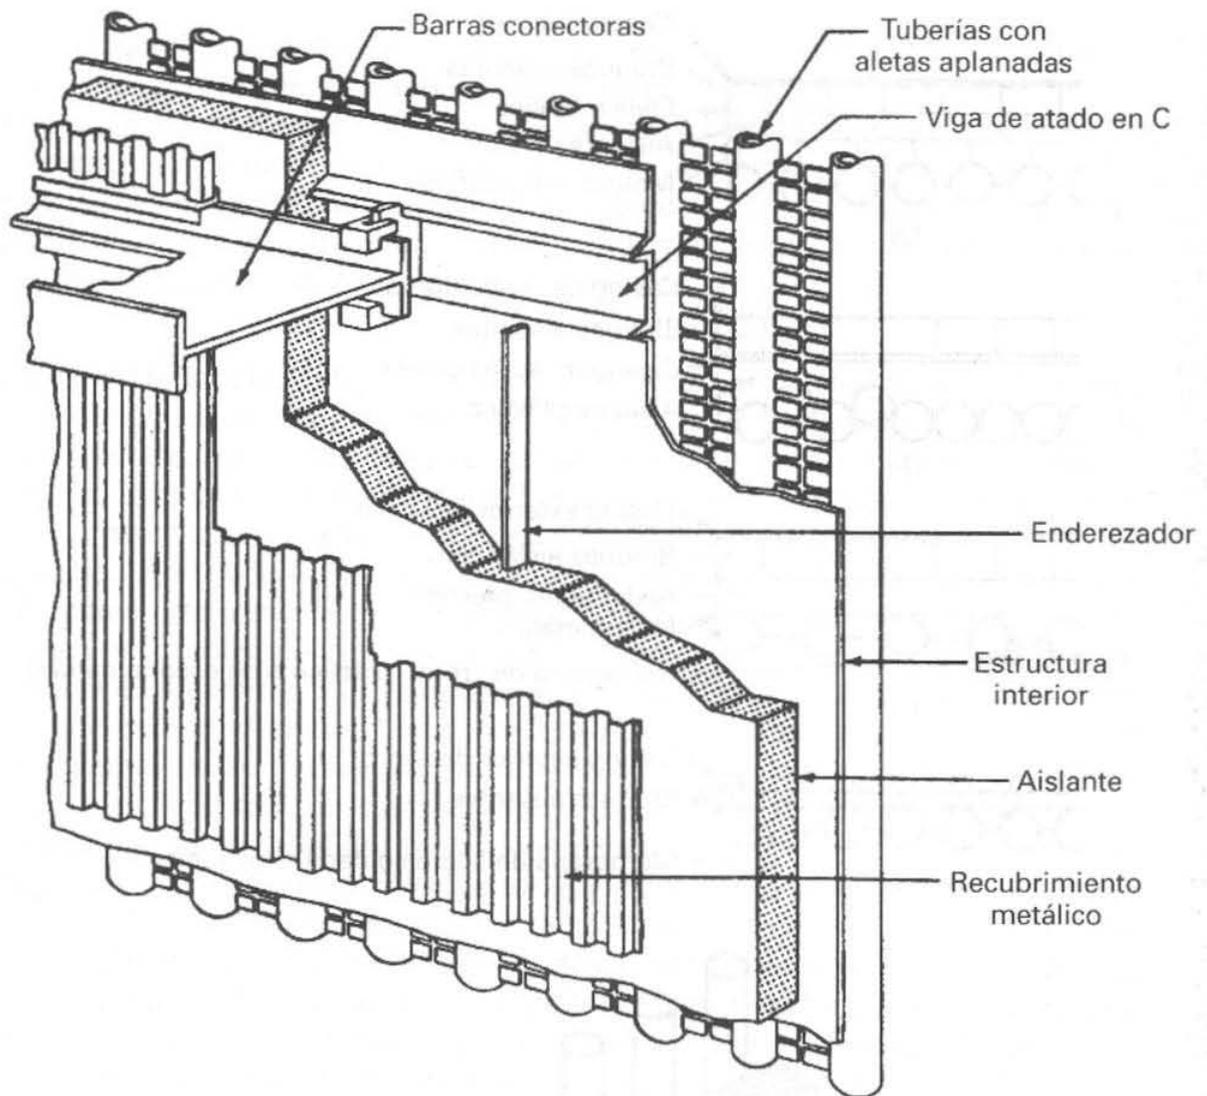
Los paneles de agua se refuerzan con soportes de acero estructural para soportar subidas anormales de presión del hogar.
